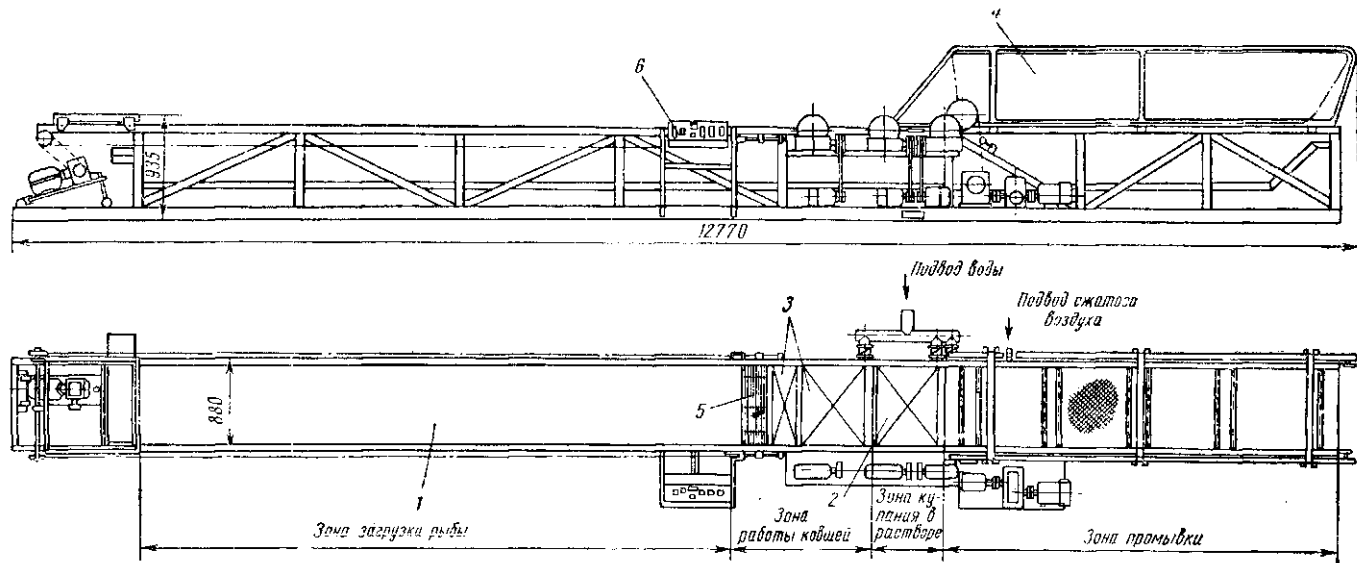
Передвижная установка для профилактической обработки рыбы:
